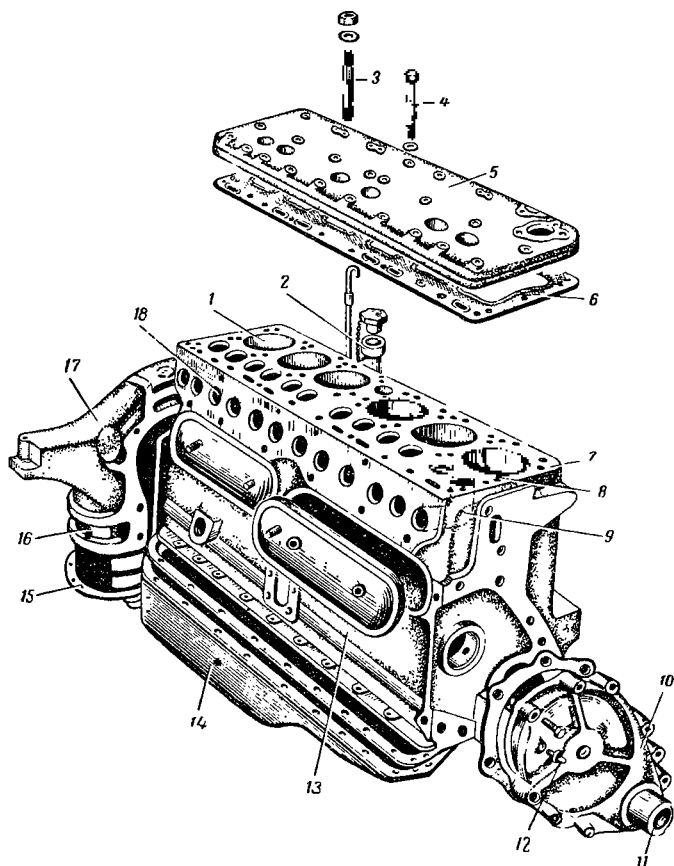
Блок цилиндров и детали двигателя ЗИЛ-120.
